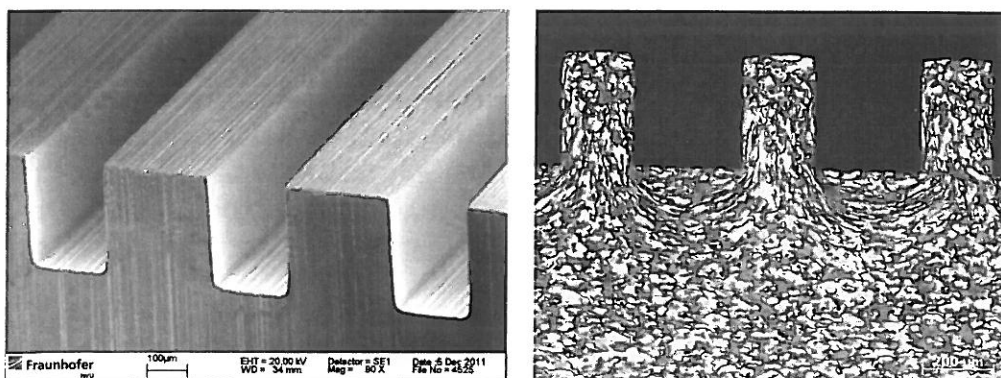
REM-Aufnahme des monolithischen Werkzeugs (links) und Schlibfbild einer umgeformten Mikrostruktur (rechts)
